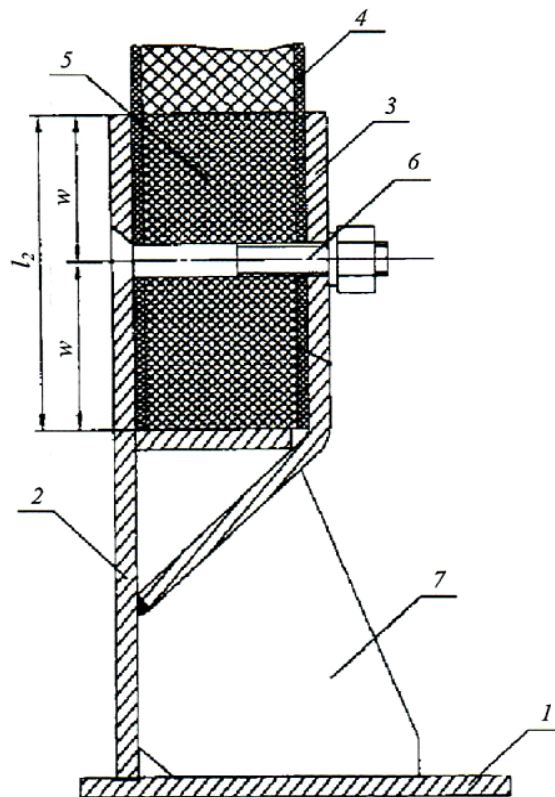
Вузол клеєболтового з'єднання перегородки з металевим корпусом
